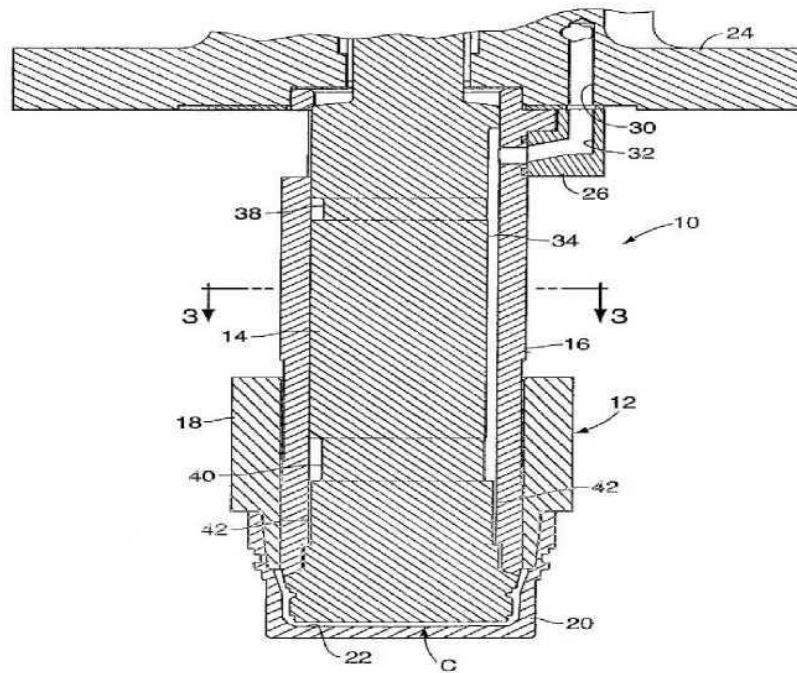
Схема механізму для формування пластмасового закупорювального засобу
